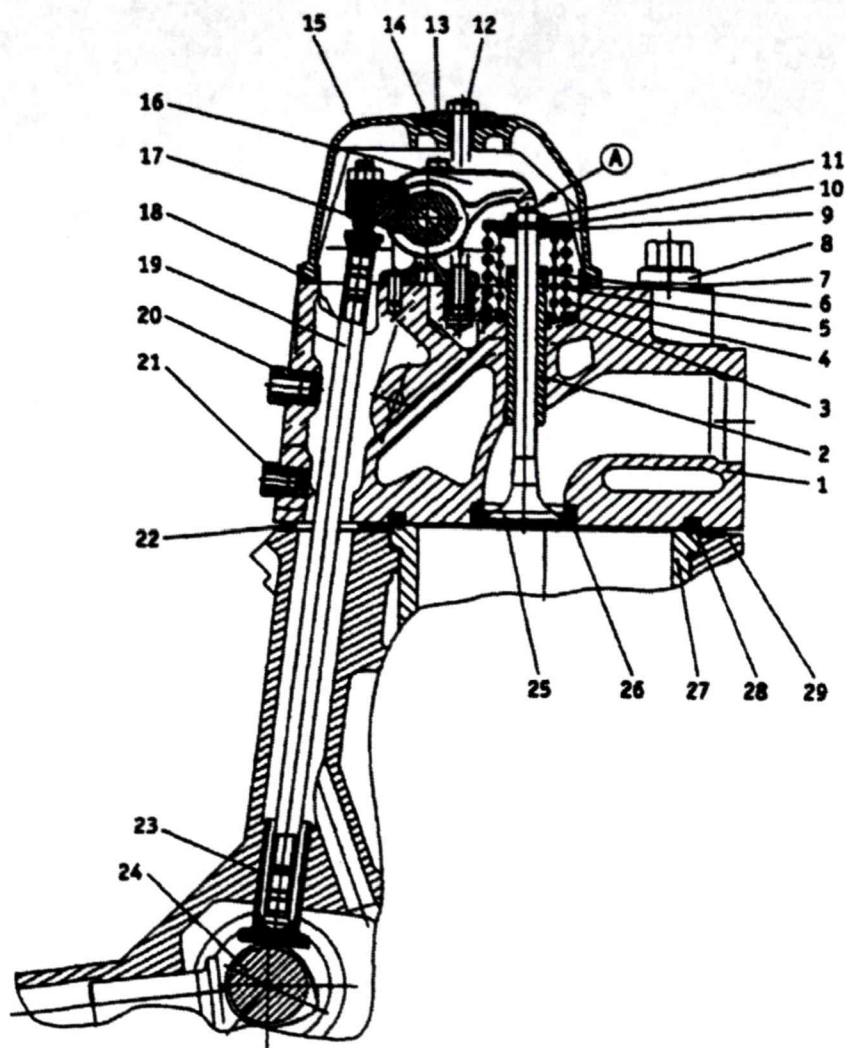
Механізм газорозподілу двигуна КамАЗ-740 1 - голівка циліндрів; 2 - напрямна втулка; 3 - шайба; 4,5 - пружини; 6 - манжета клапана; 7 - шайба; 8 - болт; 9 - тарілка пружин; 10 - втулка; 11 - сухар; 12 - болт кріплення кришки; 13 - шайба; 14 - віброізоляційна шайба; 15 - кришка голівки циліндра; 16 - коромисло; 17 - стійка коромисел; 18 - прокладка; 19 - штанга; 20 – укрупень кріплення впускного колектора; 21 – укрупень кріплення водяної труби; 22 - прокладка; 23 -штовхальник; 24 - розподільний вал; 25 - випускний клапан; 26 - сидло випускного клапана; 27 - гільза циліндра; 28 - кільце; 29 - блок циліндрів; А - тепловий зазор.
